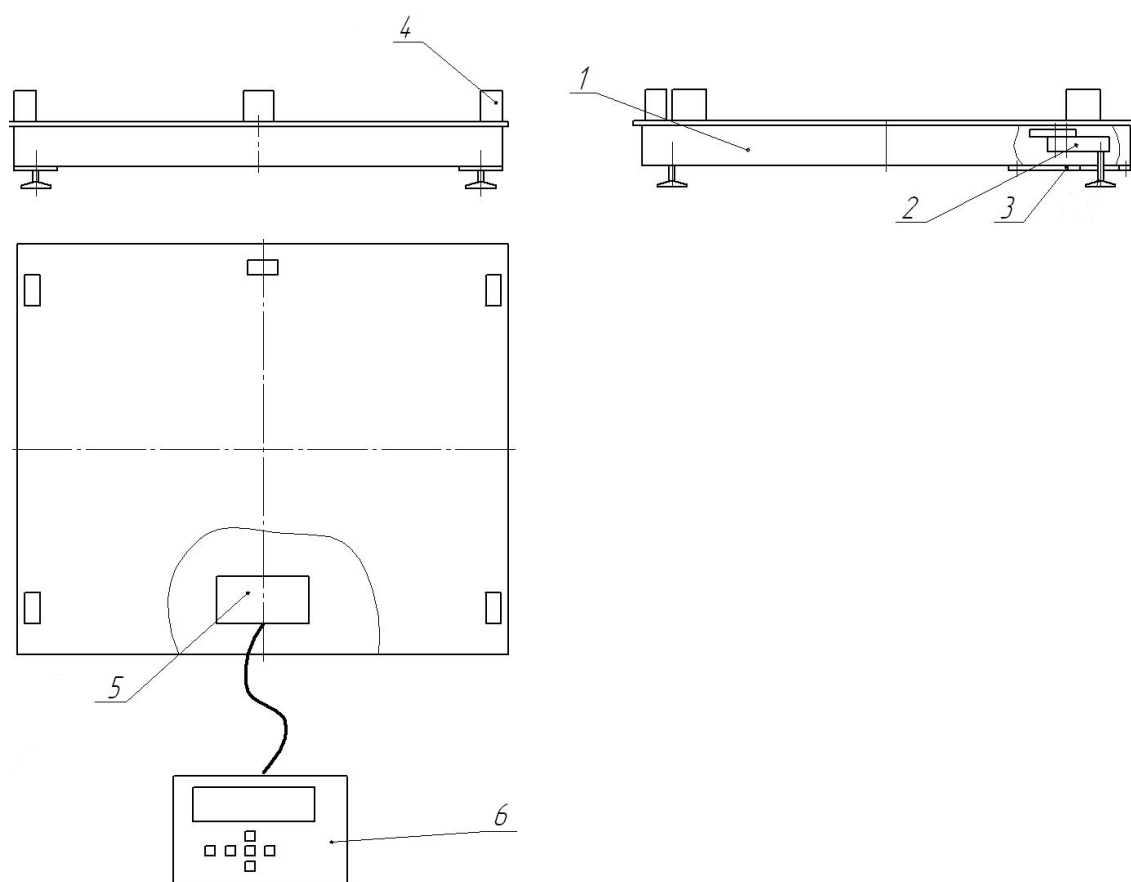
Общий вид весов (1 – платформа; 2 – весоизмерительный тензорезисторный датчик; 3 – крышка; 4 – элементы для установки перил; 5 – соединительная коробка; 6 – электронное весоизмерительное устройство)
